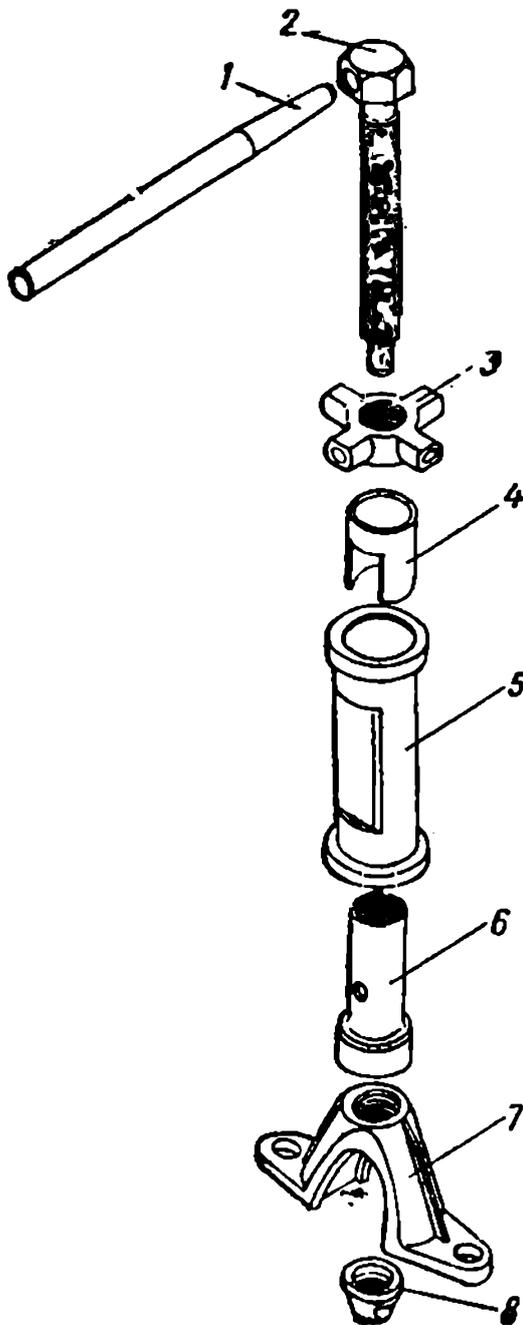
Приспособление для установки и демонтажа торсионов, опорных катков и направляющих колес:
